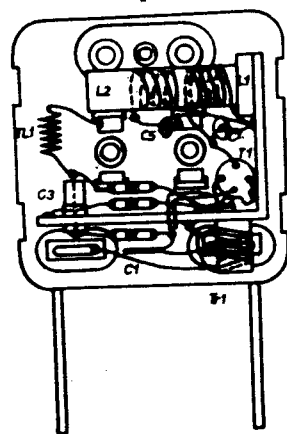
Základní zapojení měniče kmitočtů TAMV 61
